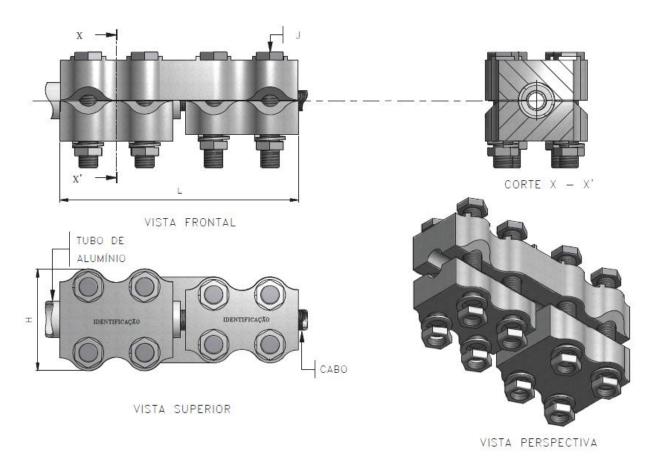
Vista do Conector Emenda para Tubo e Cabo de Alumínio
